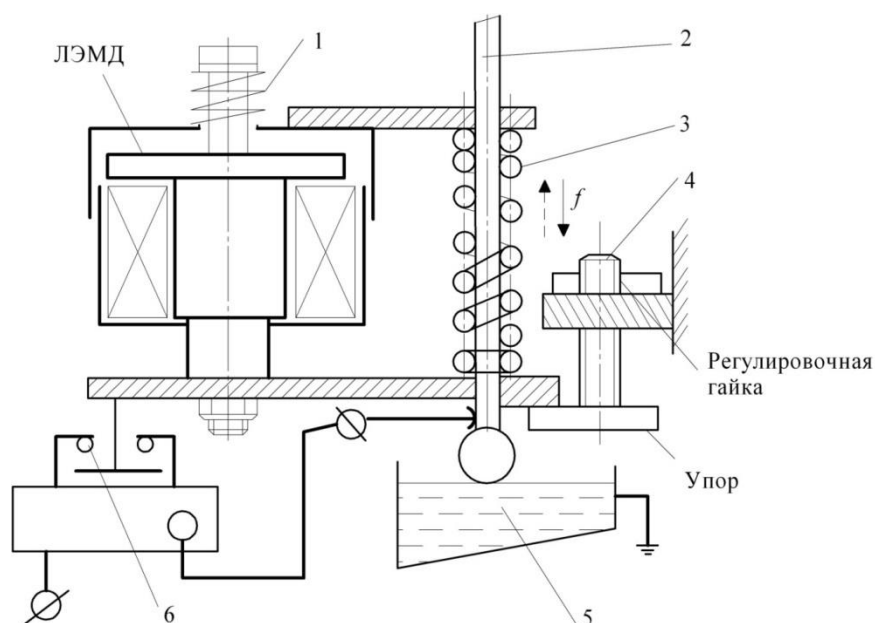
Схема дозированной наплавки в режиме коротких замыканий с помощью ЛЭМД: 1 - возвратная пружина; 2 - электрод; 3 - зажим-пружина; 4 - регулировочный упор; 5 - ванна расплава; 6 – контакт
